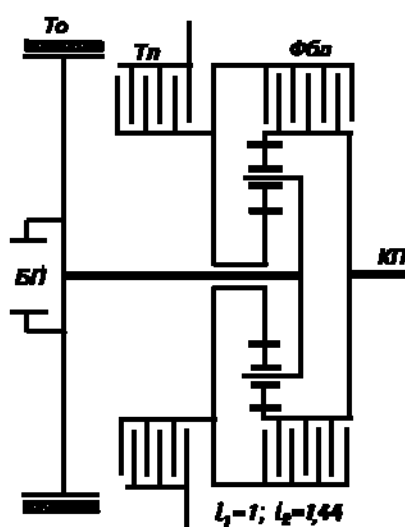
Кинематическая схема планетарного механизма поворота боевой машины пехоты БМП-2
